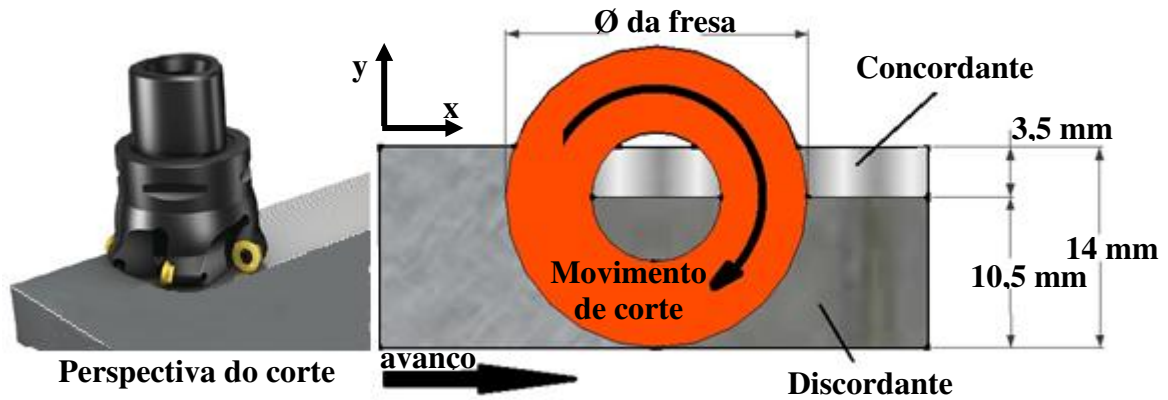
Esquema cinemático do corte frontal, faceamento de topo e posicionamento da fresa, em que predomina o corte discordante
